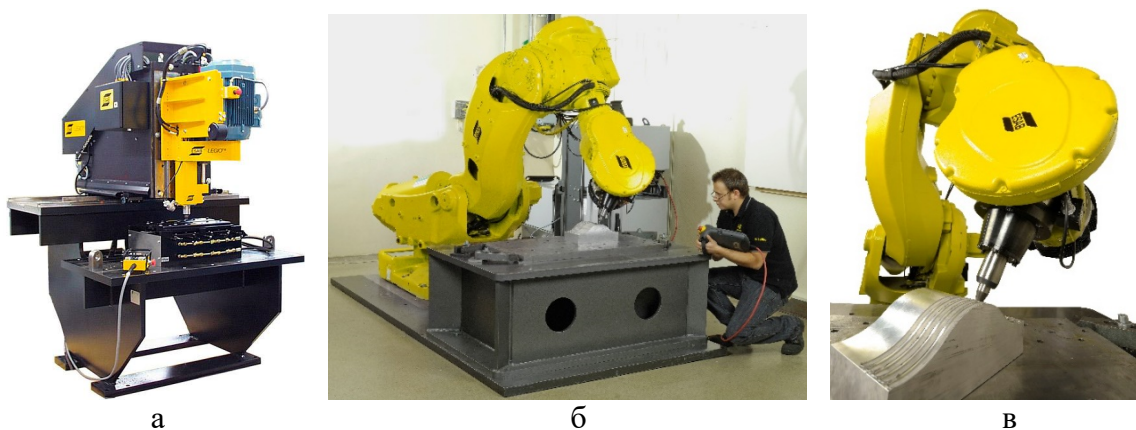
Внешний вид сварочной машины Legio™ (а) и роботизированной сварочной головки Rosio™ (б, в), предлагаемых концерном ESAB [11]
